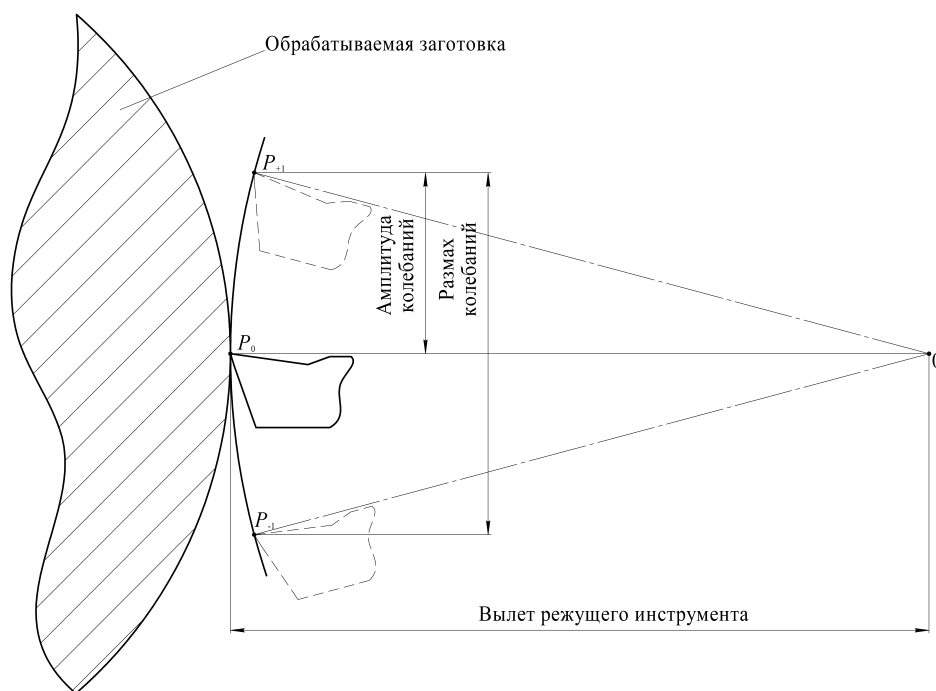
Геометрия движения режущего инструмента при формировании профиля микронеровностей обрабатываемой поверхности
